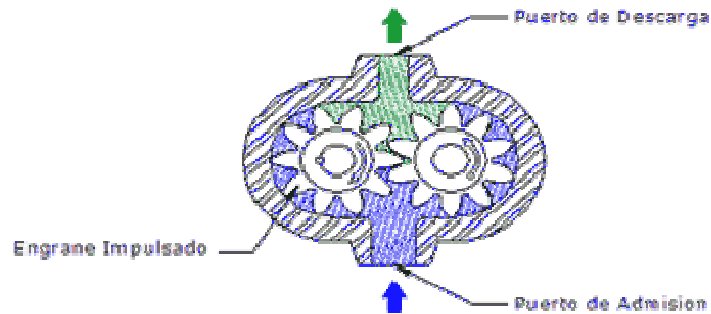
, Bomba de Engranajes, Fuente, www.techniforum.com
